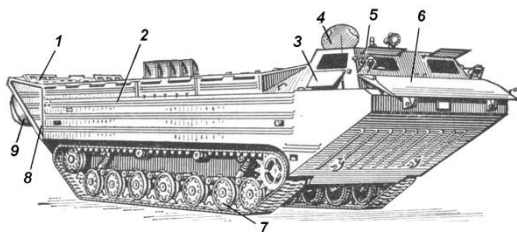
Загальний вигляд транспортера ПТС-2: 1 – апарель; 2 – корпус; 3 – відкидний щит; 4 – люк; 5 – кабіна; 6 – хвилевідбивний щит; 7 – гусеничний рушій; 8 – відкидний борт; 9 – обладнання для самообкопування
